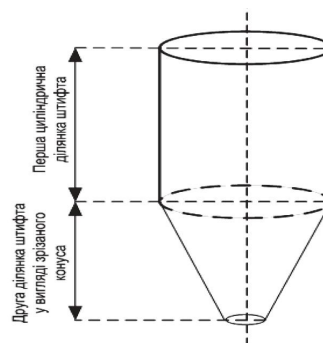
Схема поверхні циліндро-конічного штифта.
